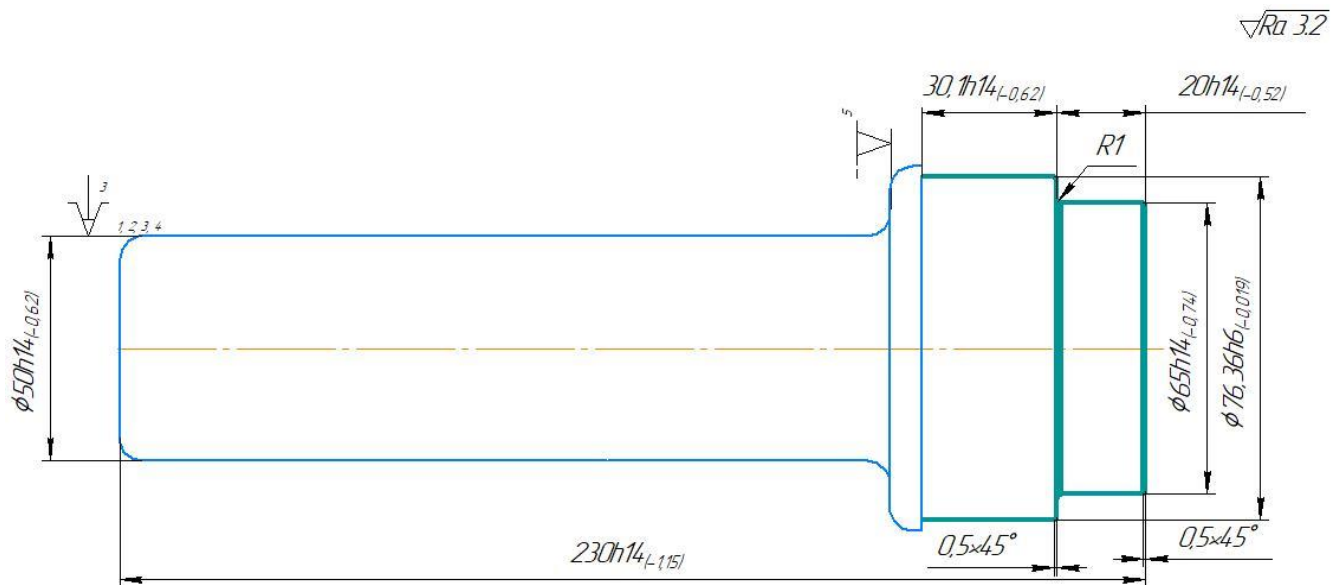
Ескізи обробки заготовки на операції 25
